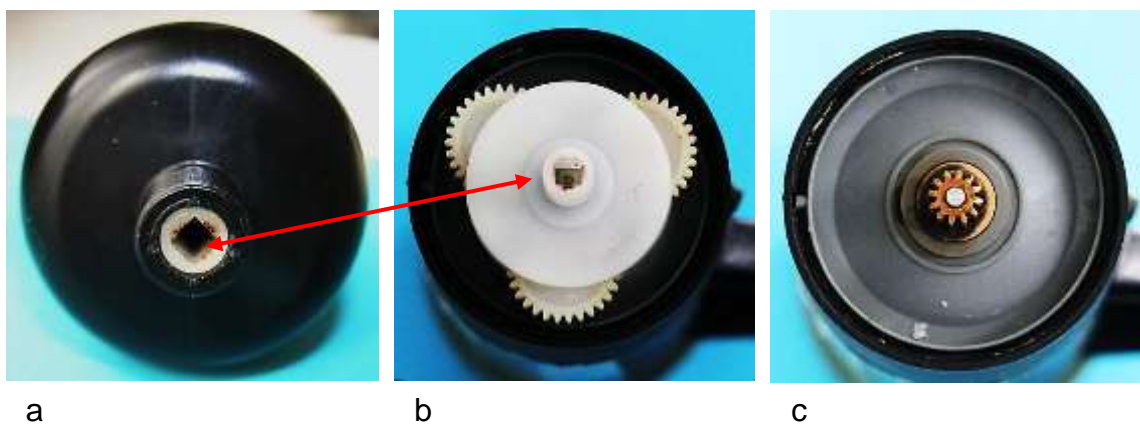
Vierkanthülse zum Antrieb des Planetenträgers: a) Position im Deckel, b) Rotierender Planetenträger (abgenommener Deckel), c) Lagerschild mit dem Sonnenrad auf der Polradwelle
